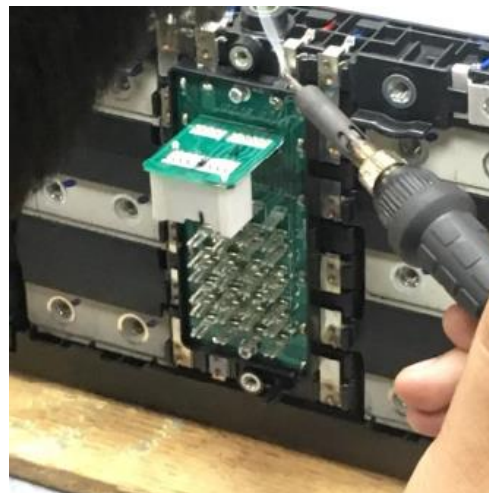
Placa del módulo de la batería. Fuente: Autores.
